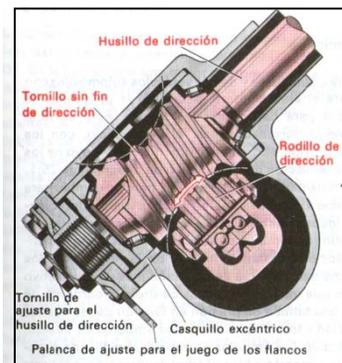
Mecanismo de tornillo sin fin con rodillo.
